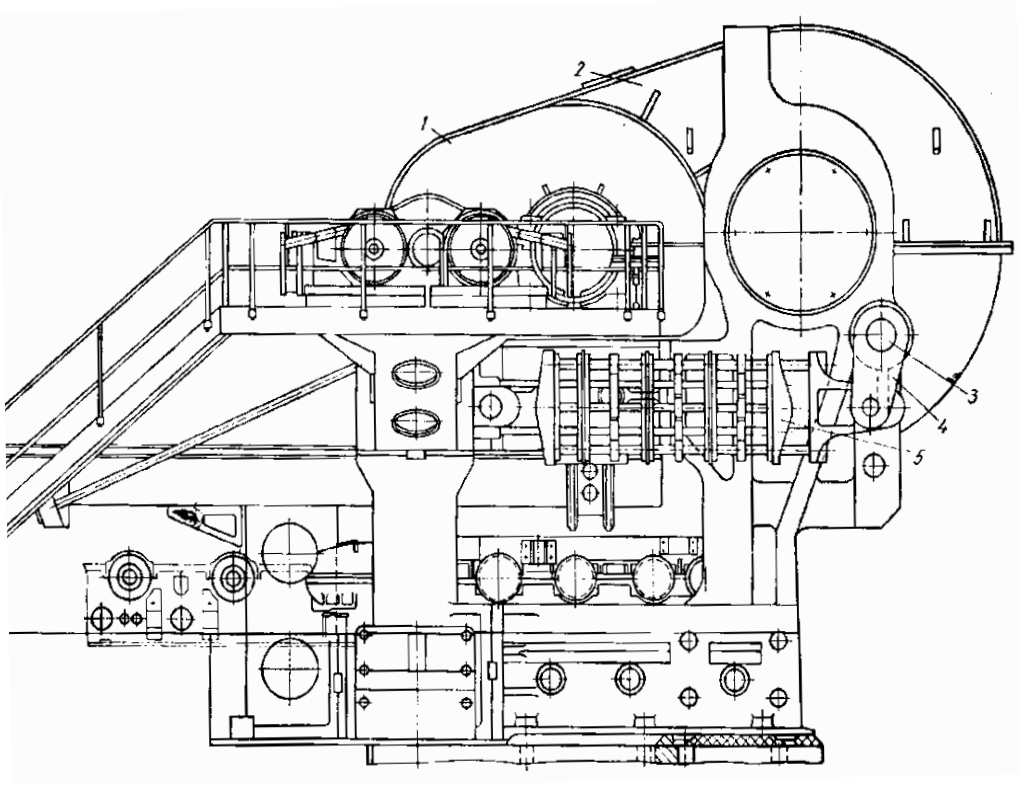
Загальний вигляд ножиць з верхнім різом
